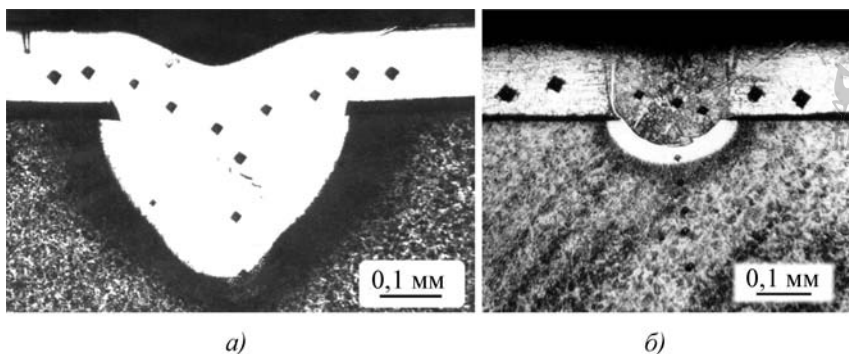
Усадочная раковина в сварных точках, выполненных точечной лазерной сваркой.  $\times 100$
